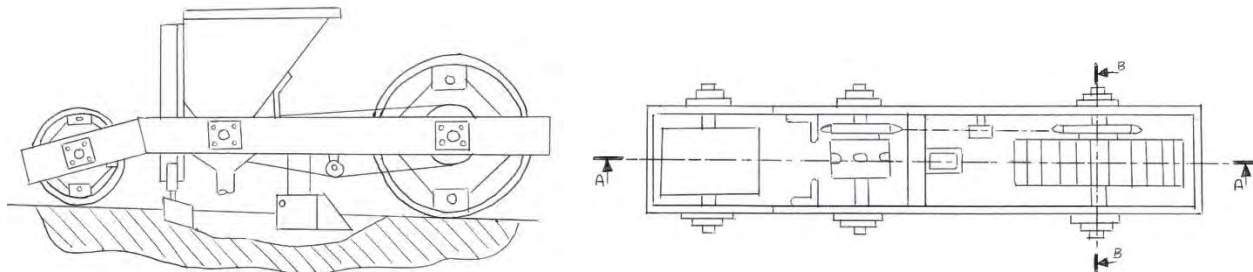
Vista lateral y superior del proyecto preliminar 02
